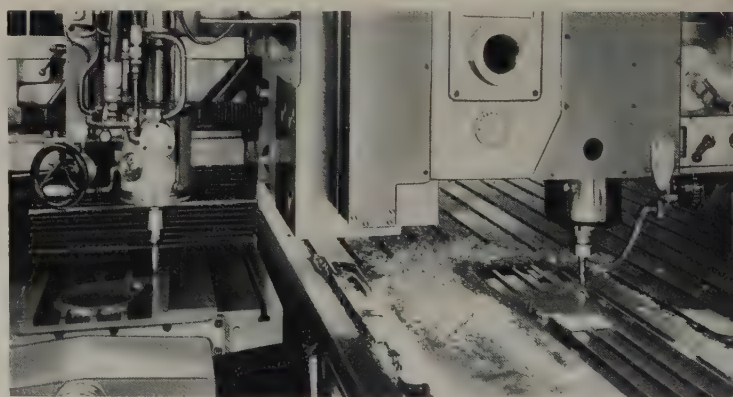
Abtastkopf am Modell (links) und Fräskopf mit senkrechter Frässpindel (rechts) einer Kopierfräsmaschine bei der Bearbeitung eines Flügelbleches
